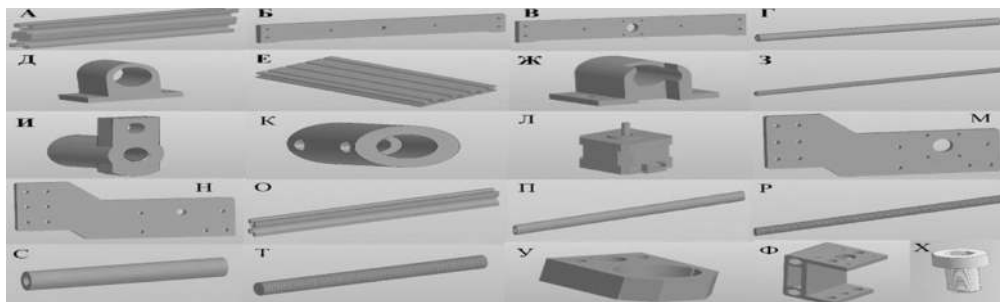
Основные конструкционные элементы лабораторного трехкоординатного ударно-точечного маркировочного станка с ЧПУ
